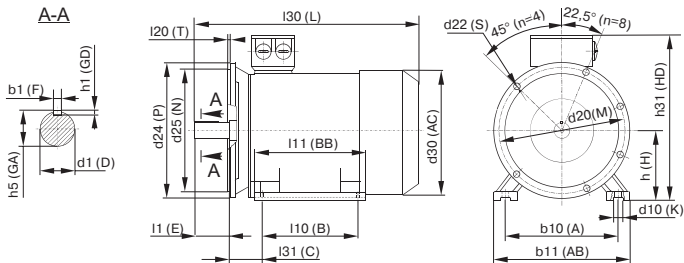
Размеры двигателей монтажного исполнения IM 2081 / Figure 2 – Motor dimensions of IM 2081 mounting version / Сурет 2 – IM 2081 монтаждық орындалым қозғалтқыштарының өлшемдері
